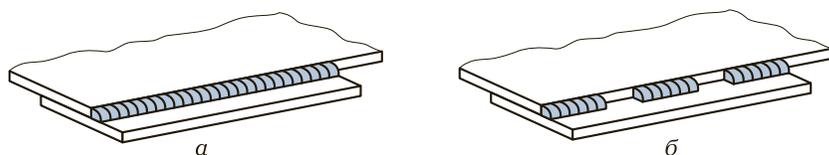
Непрерывный (а) и прерывистый (б) сварные швы
